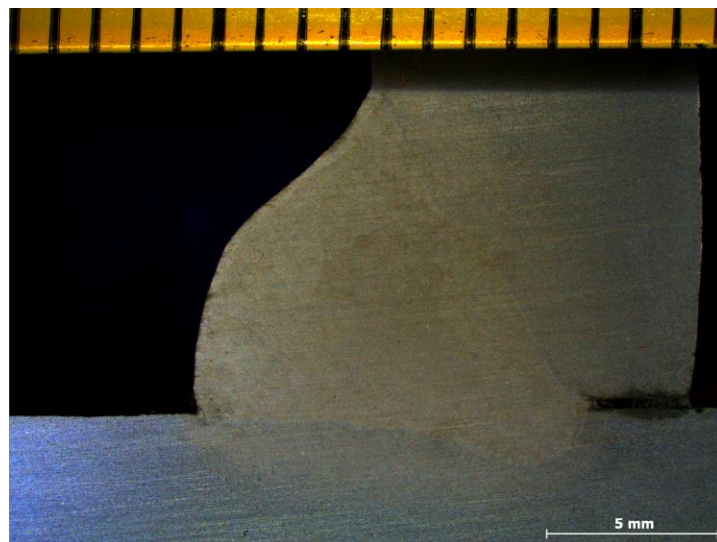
Makroizbrusak uzorka 2. - CV MAG
